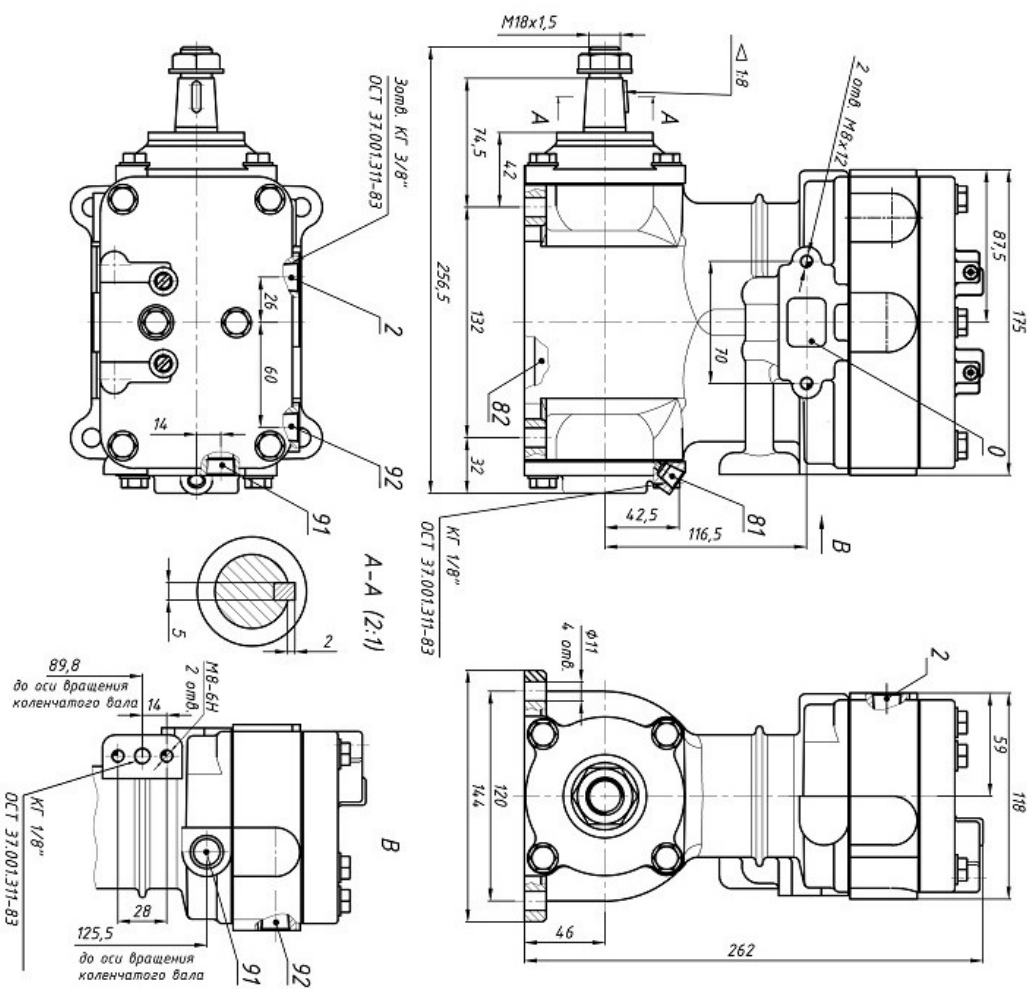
Присоединительные и установочные размеры компрессора АМ.3509015-540.
